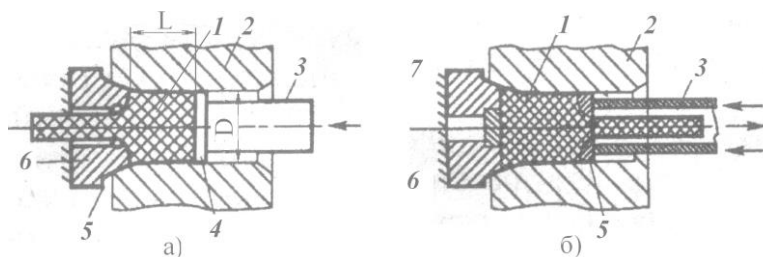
Схемы прессования: а – прямого; б – обратного: 1 – заготовка; 2 – контейнер; 3 – пуансон; 4 – пресс-шайба; 5 – матрица; 6 – матрица-держатель; 7 – заглушка; L – длина заготовки, м; D – диаметр контейнера, м.
